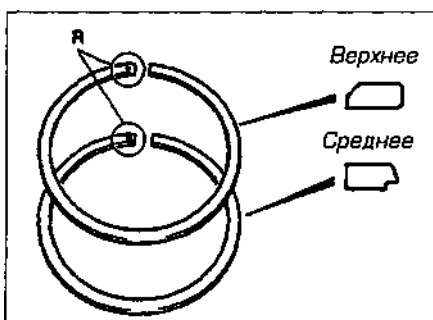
Установите компрессионные кольца маркировкой вверх с помощью приспособления
